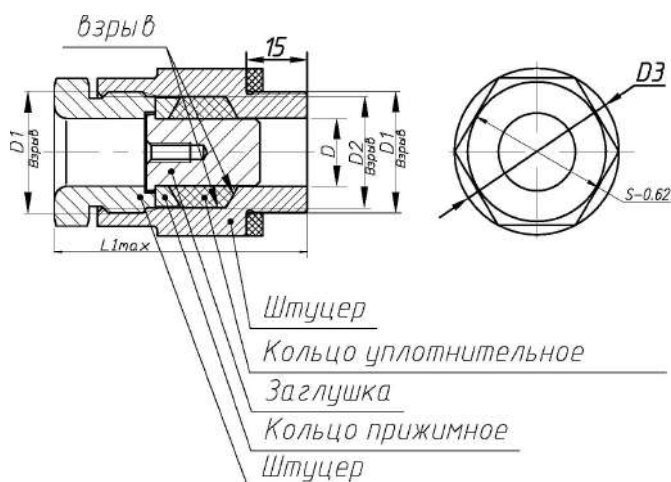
Конструкция кабельного ввода ExKV для открытой прокладки кабеля.
